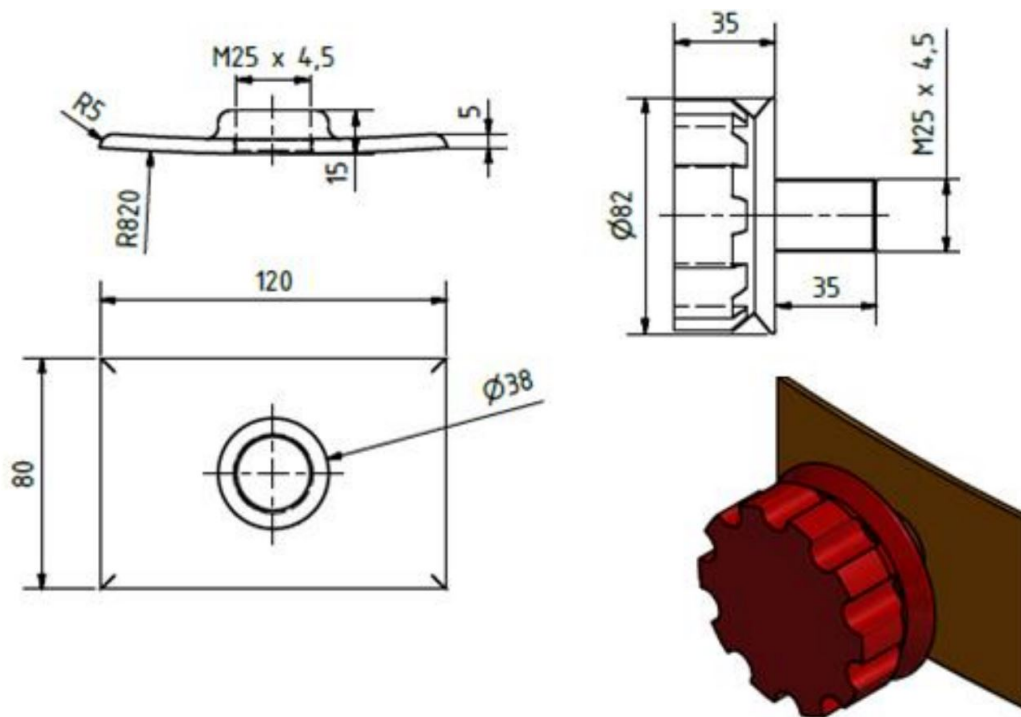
Diseño y dimensiones del perno y placa roscada de cierre. Fuente [28].
